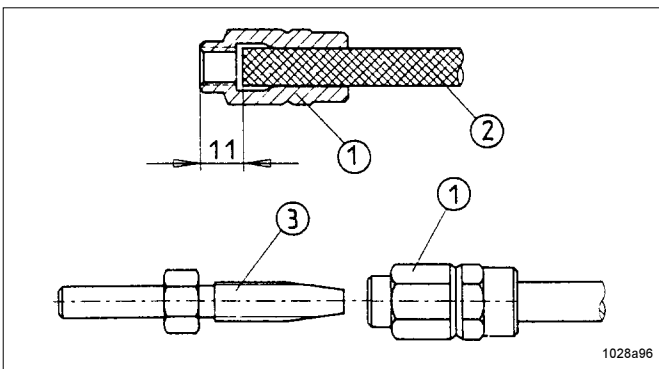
Vormontage der Schraubhülsen und Schlauchstutzen auf die Hauptleitung
